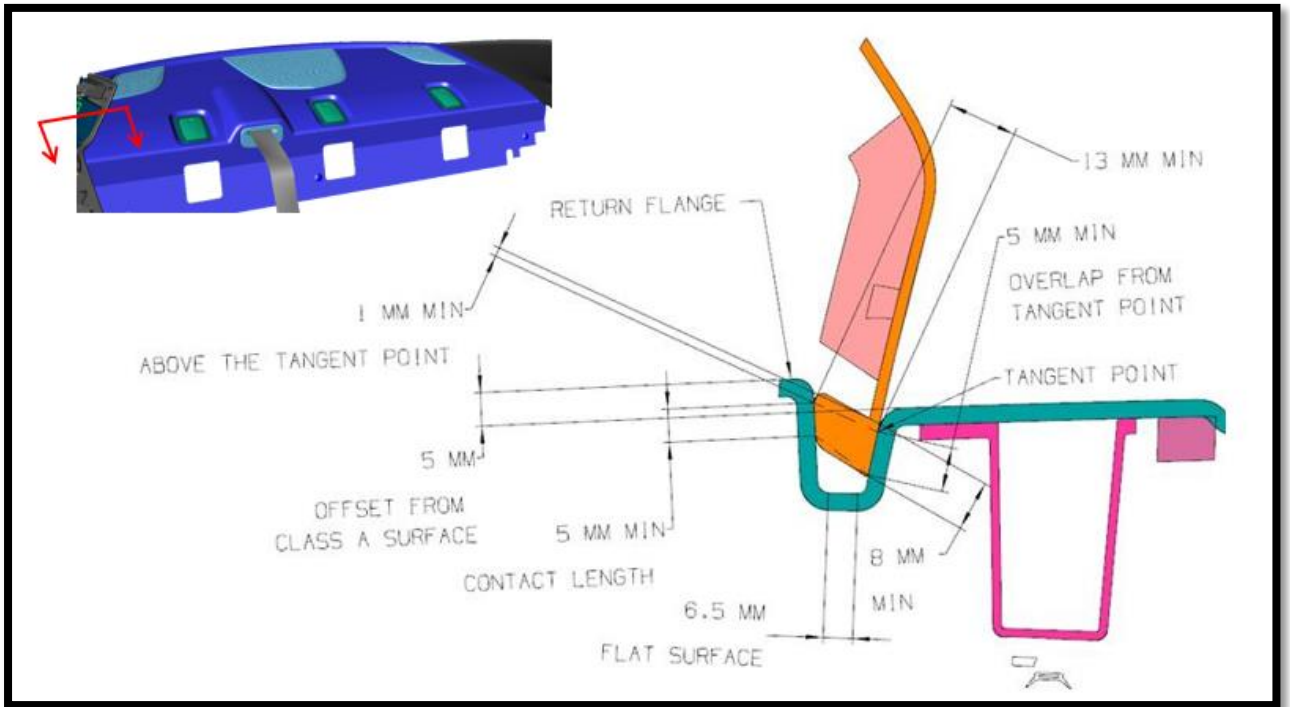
Sección típica para interface con cubierta lateral de plástico. [4]
